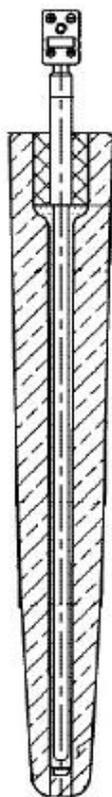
Чертеж ТП в сборе с гильзой мод. МТ00083 (МТ00554) без стопорной пластины
